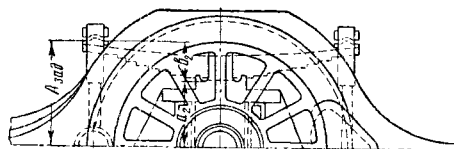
Проверка и регулировка рессорного подвешивания сцепных осей
